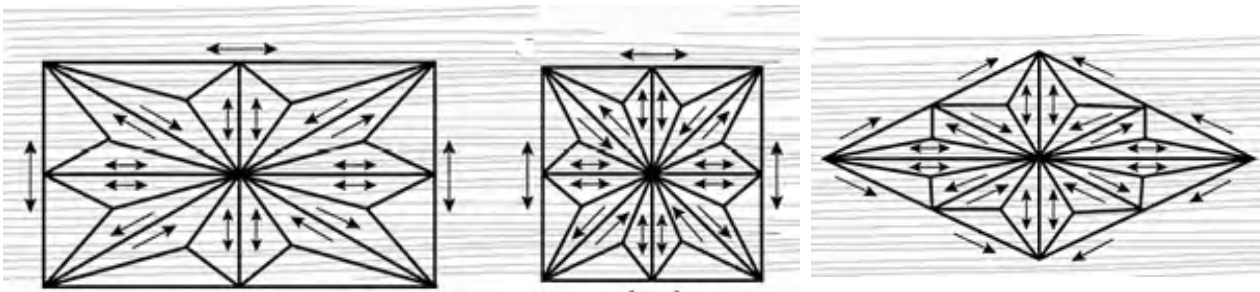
Разметка и направление движения ножа (фон указывает направление волокон древесины)
